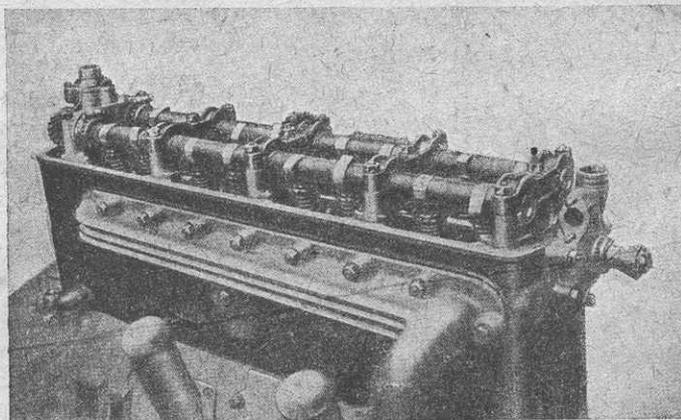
Восемьцилиндровый двигатель «Хорьх» (головка цилиндров снята).
